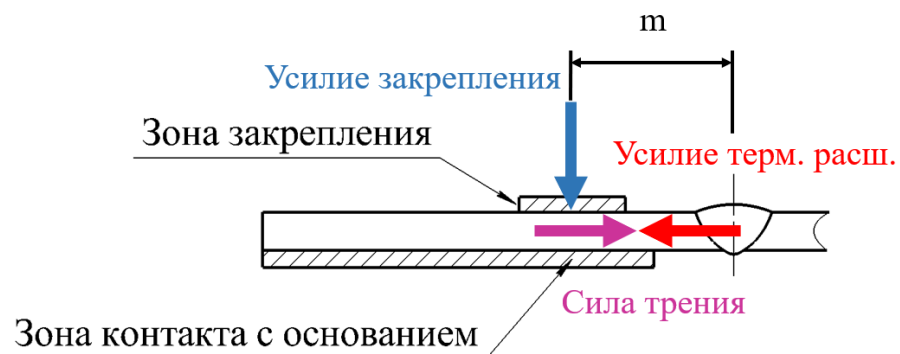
Схема закрепления и усилия в детали при сварке
